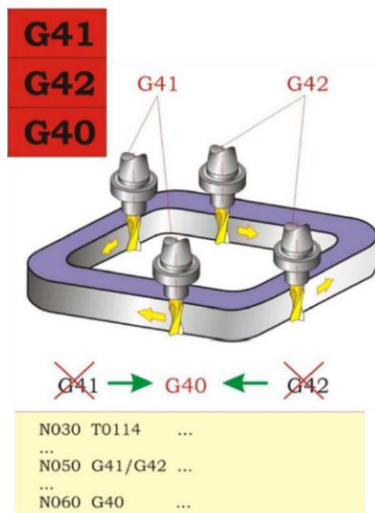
Корекція на радіус інструмента справа та зліва під час фрезерного оброблення
